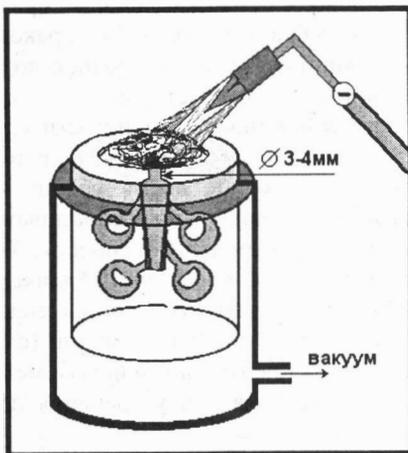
Схема плавки и заливки расплава при вакуумном литье
